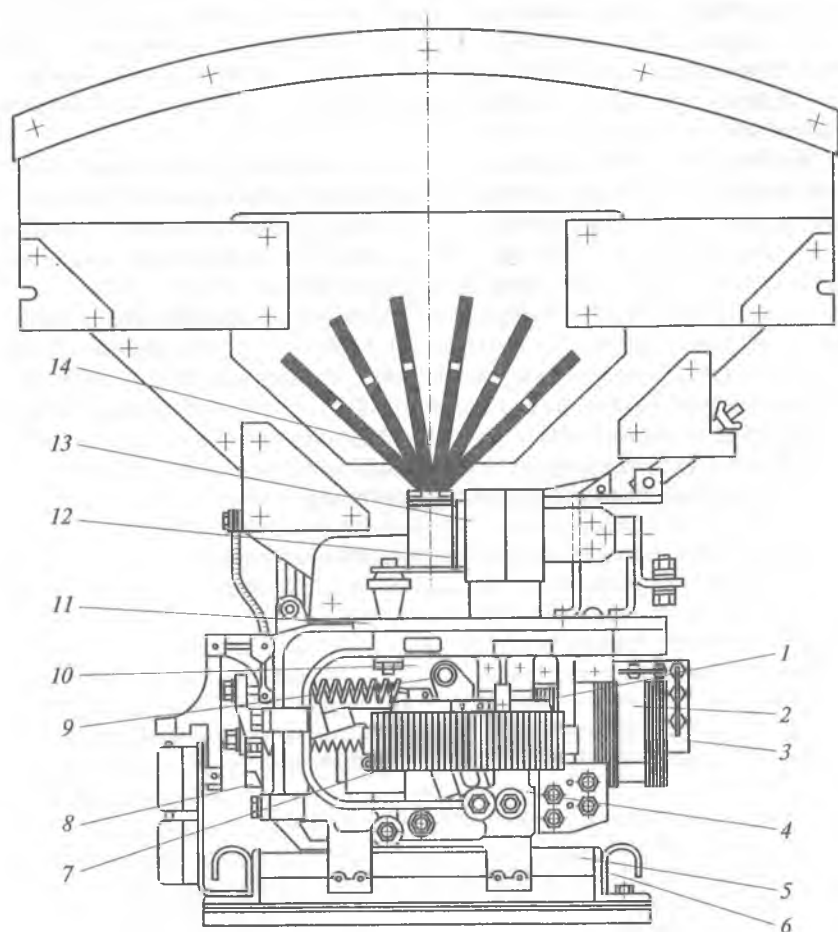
Быстродействующий выключатель БВП-5-02:
